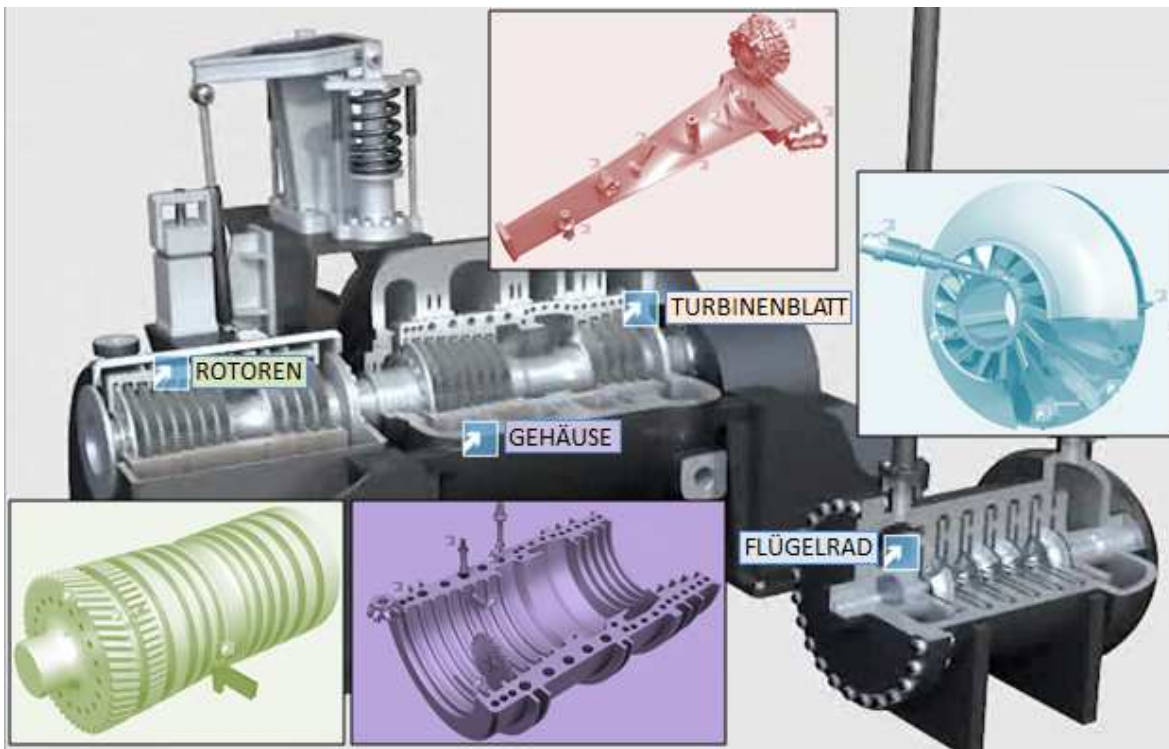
Darstellung der zu bearbeitenden Hauptkomponenten einer Gasturbinenanlage mit Rotoren, Gehäuse, Turbinenblatt und Flügelrad mit Hyperlinks, welche zu den einzelnen Komponenten und Werkzeugen führen¹⁷
